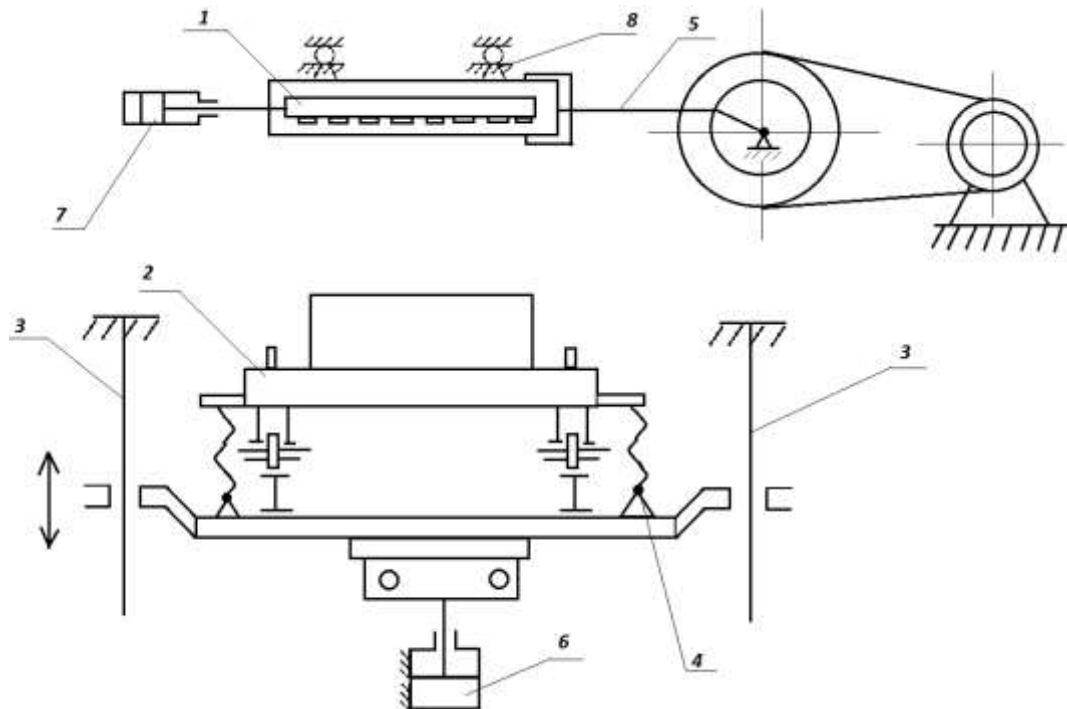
Швидкісний алмазно-штрипсовий розпилювальний верстат СМР-077
